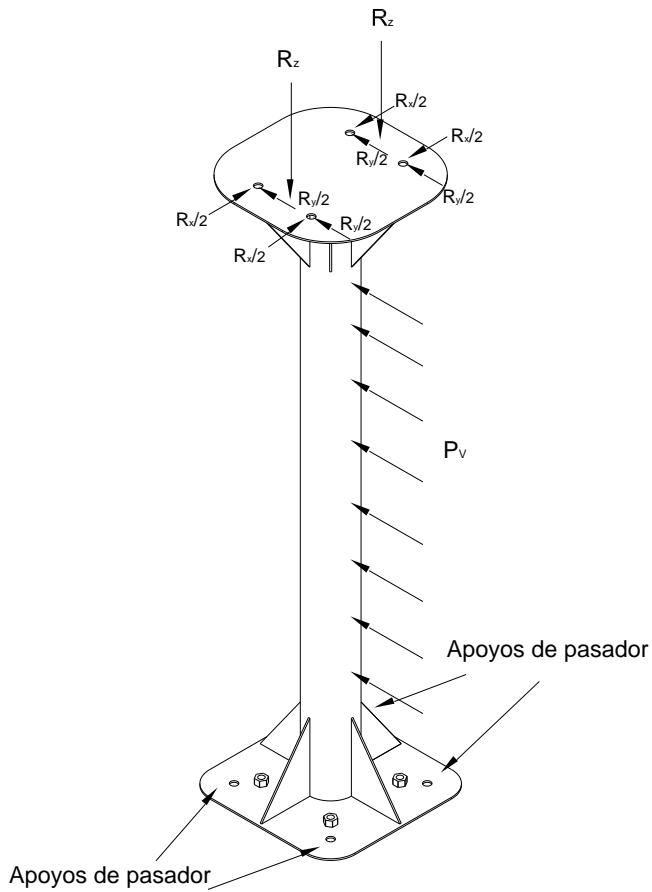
Cargas y tipos de apoyo que actúan en la columna y membranas rigirizadoras.
